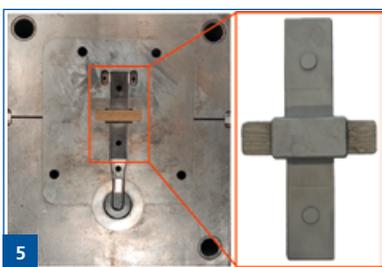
Fixierung der Holzeinleger im Reckgießwerkzeug (links); Hybrides Aluminium-Holz-Gussbauteil (rechts)
